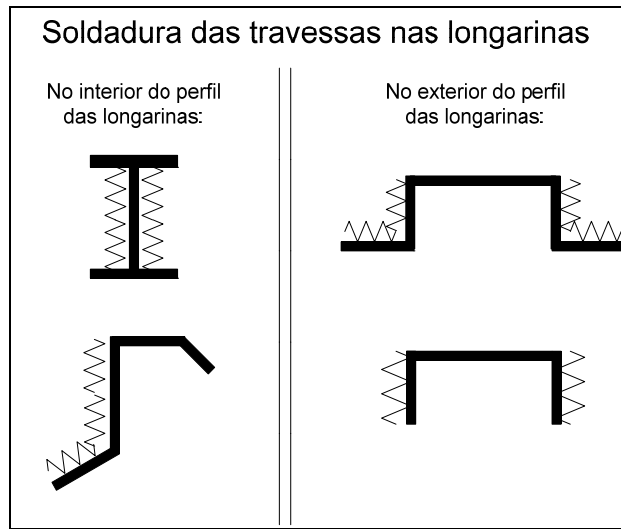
Modo de soldadura das travessas nas longarinas
